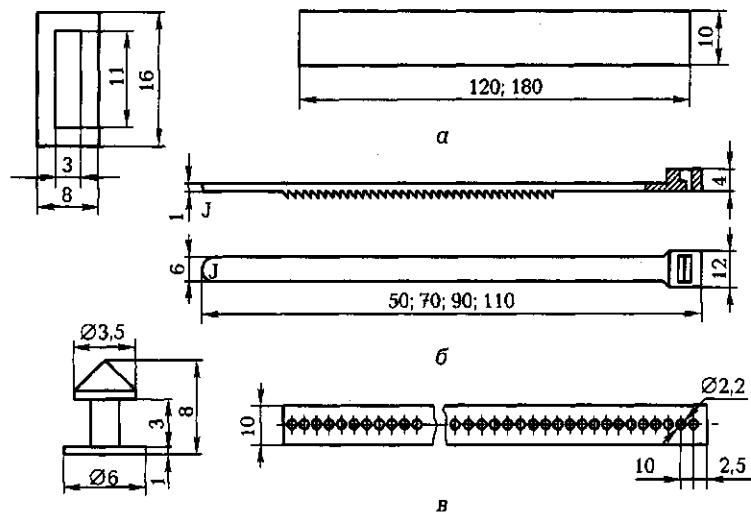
Изделия для крепления кабелей, труб и проводов:
